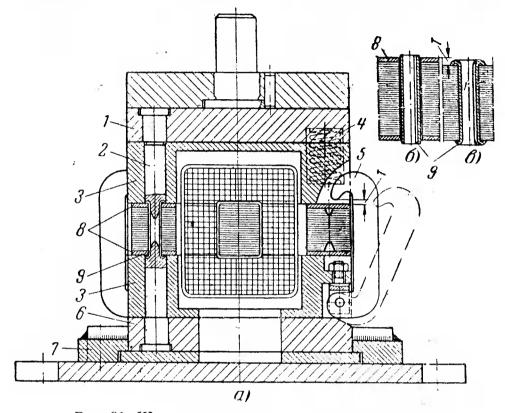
Штамп для прессовки магнитопроводов и развальцовки крепежных трубочек.
